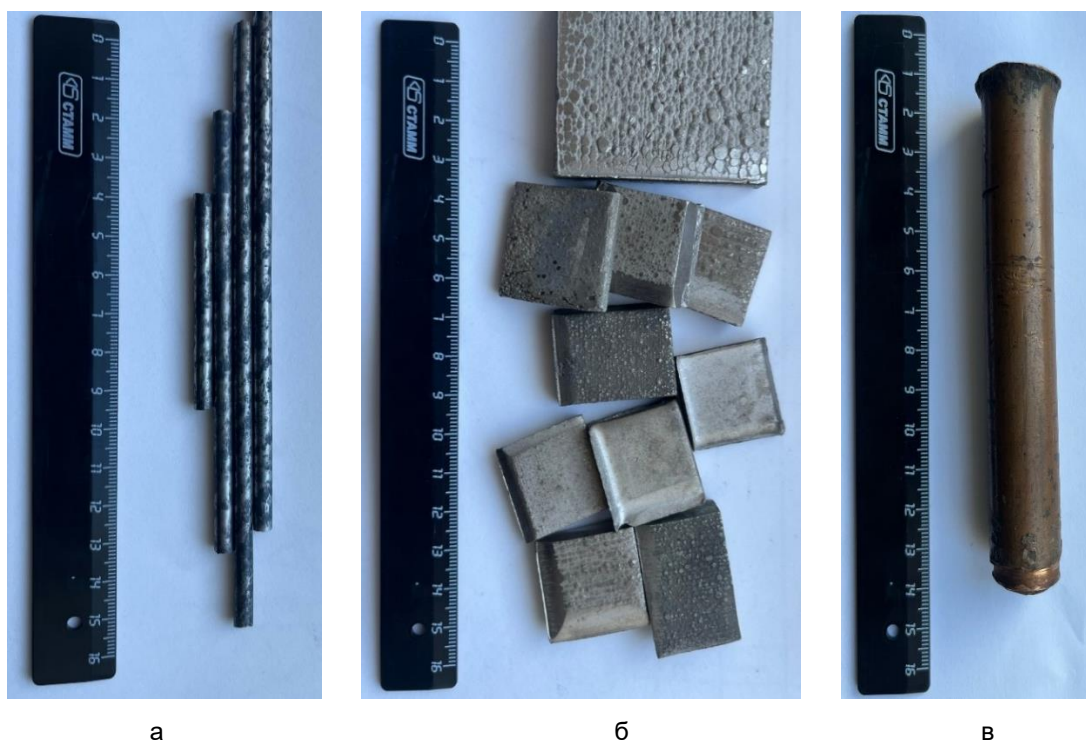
Образцы металлоотходов: а – пруток вольфрамовый; б – пластина никелевая; в – пруток медный
